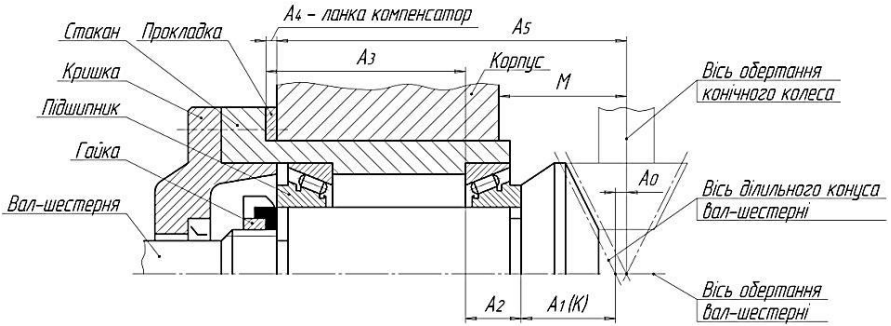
Схема РЛ, яка визначає точність збігу вершин ділильного конуса вала-шестірни з віссю обертання кінцевого колеса
